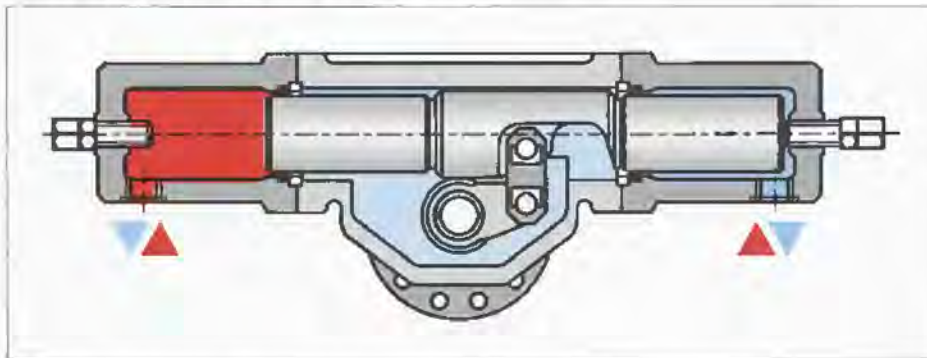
Поворотный гидродвигатель с шатунно-кривошипным приводом и поршнем, совершающим возвратно-поступательное движение
